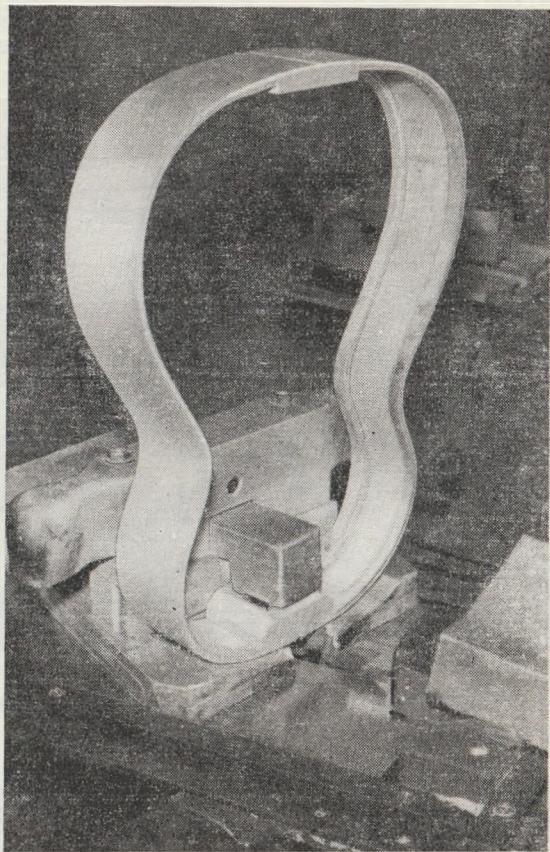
Выборка гнезда в рамке корпуса гитары на специальном фрезерном станке
